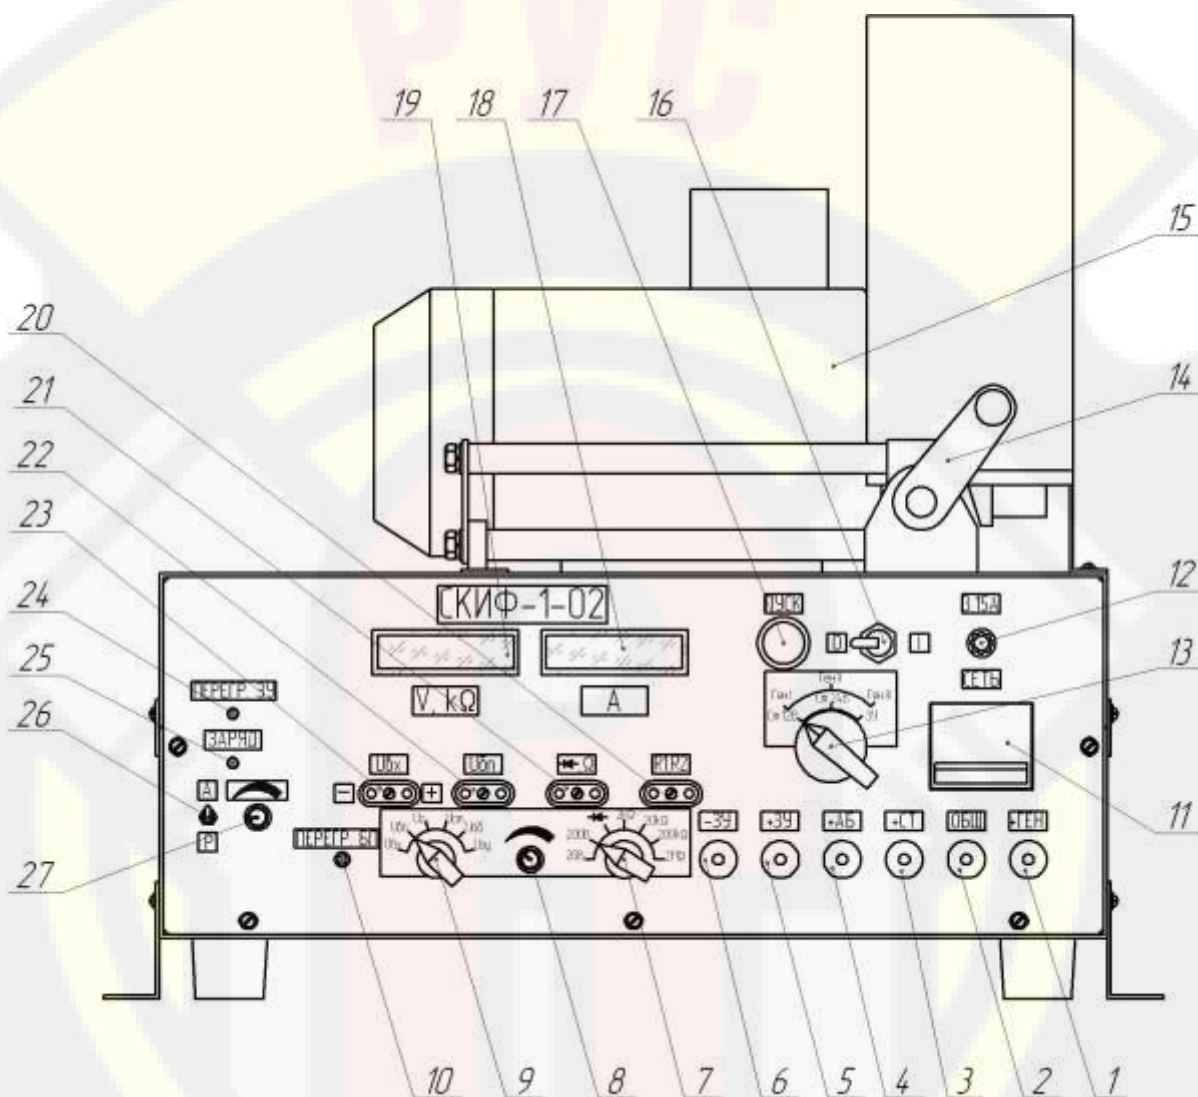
Внешний вид станда диагностического SKIF-1-02
